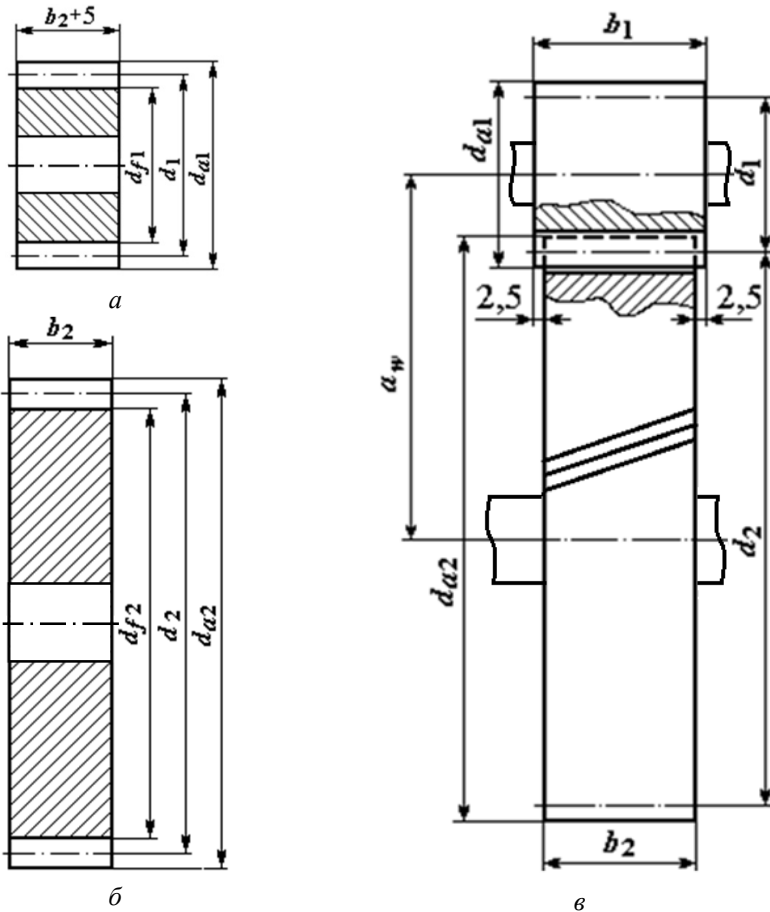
Эскизы шестерни (а), зубчатого колеса (б) и зубчатого зацепления (в)
